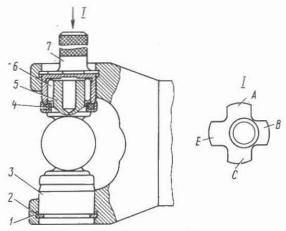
Montaje de la junta cardánica: 1 - horquilla de la junta cardánica; 2 - anillo de fijación; 3 - cuerpo del cojinete; 4 - retén; 5 espiga de la cruceta; 6 - aguja del cojinete; 7 calibre;
